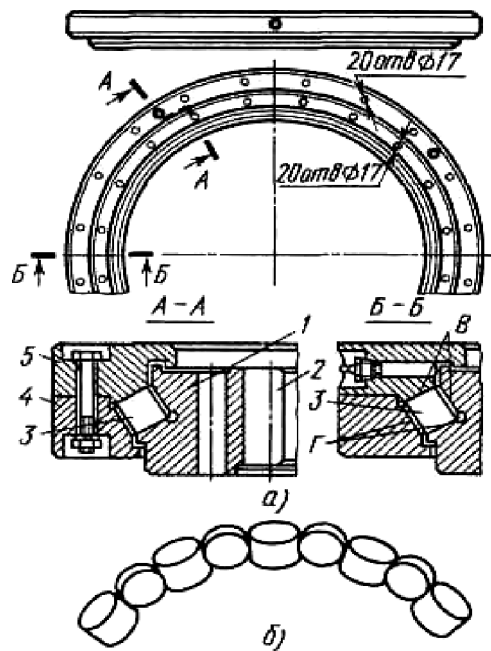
Роликовий опорно-поворотний пристрій: а – розріз А-А і Б-Б роликового кола, б – схема розташування роликів; 1 - внутрішнє кільце-вінець; 2 - зубчастий вінець; 3 – ролик; 4 і 5 - нижня і верхня півобойми; В і Г – бігові доріжки роликів
